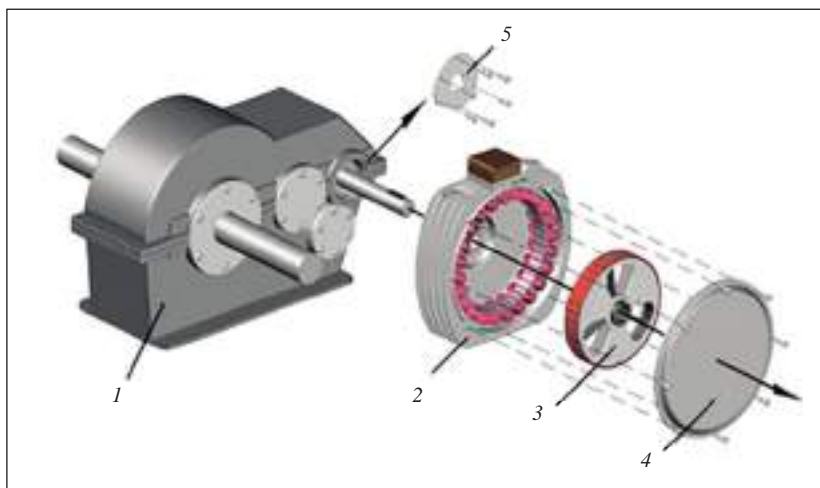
Схема установки вентильного двигателя на редуктор балансира СК:
